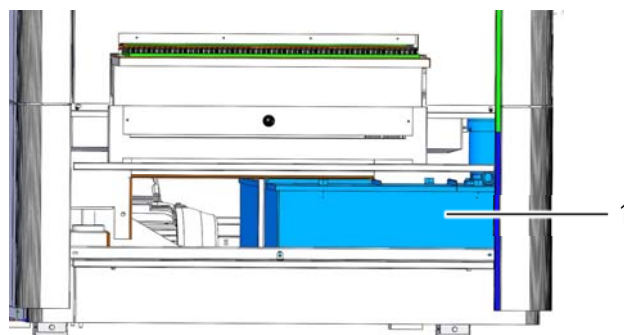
Kühlschmiermitteltank (blau, Maschinenrückseite)
